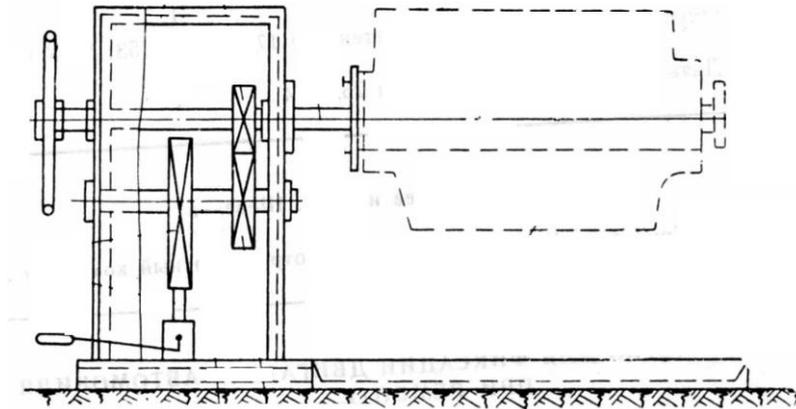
Устройство для фиксации КП и агрегатов
